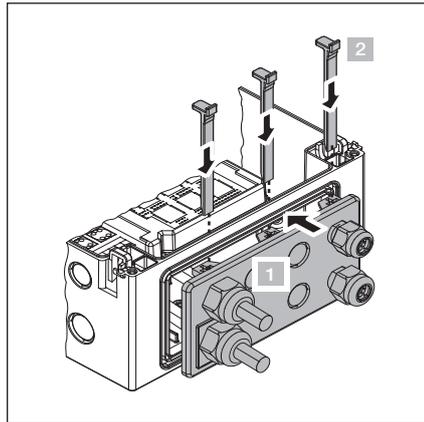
Einbau der Verschraubungsflanschplatte
